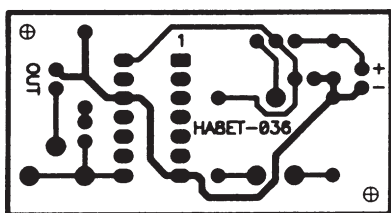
Zapojení oscilátoru podle HA8ET - 036
